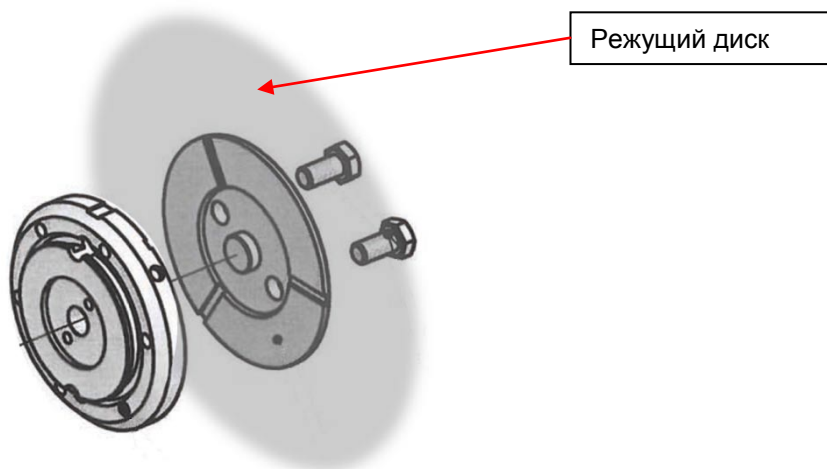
Схема монтажа фланцев крепления режущего диска (фланца крепления и прижимного фланца)
